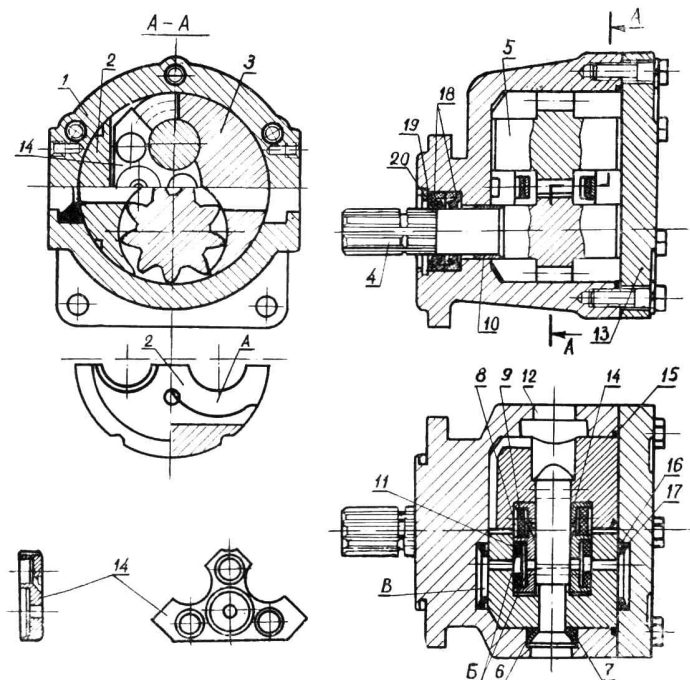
Конструкция шестеренного насоса с круглым корпусом: 1 – корпус; 2 – обойма подвижная; 3 – обойма подшипниковая; 4, 5 – шестерни зубчатые; 6 – пластина опорная; 7 – манжета; 8 – кольцо стопорное; 9 – манжета; 10 – втулка самоцентрирующаяся; 11 – манжета; 12 – напорная линия; 13 – крышка; 14 – пластики; 15 – кольцо уплотнительное; 16 – кольцо стопорное; 17 – манжета круглая; 18, 19, 20 – сальники самоподжимные с креплением
